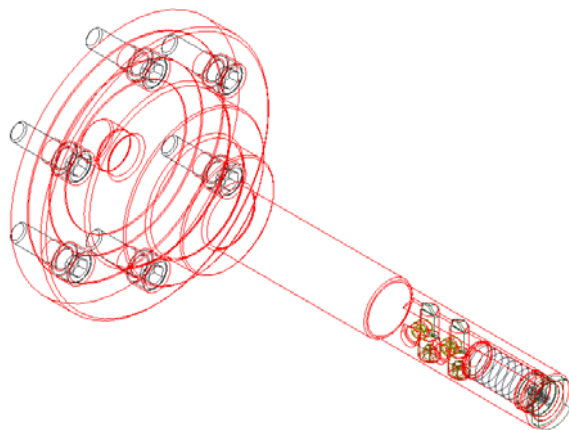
Борштанга в сборе с элементами крепления и резцом в каркасном изображении.
